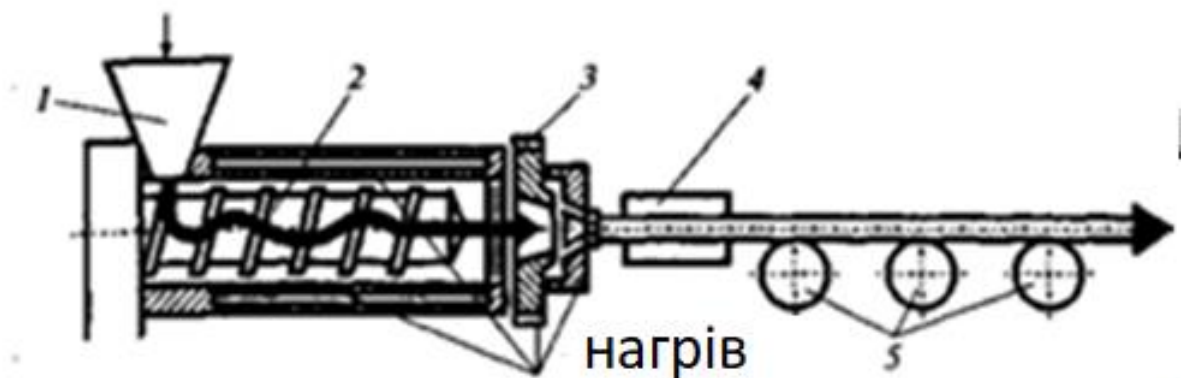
Схема роботи екструдера під час виробництва труб: 1 - завантажувальний бункер; 2 – шнек; 3 - формуюча головка; 4 - калібруюча насадка; 5 - пристрій, що тягне; 6 - пустоутворювач "дорн"
